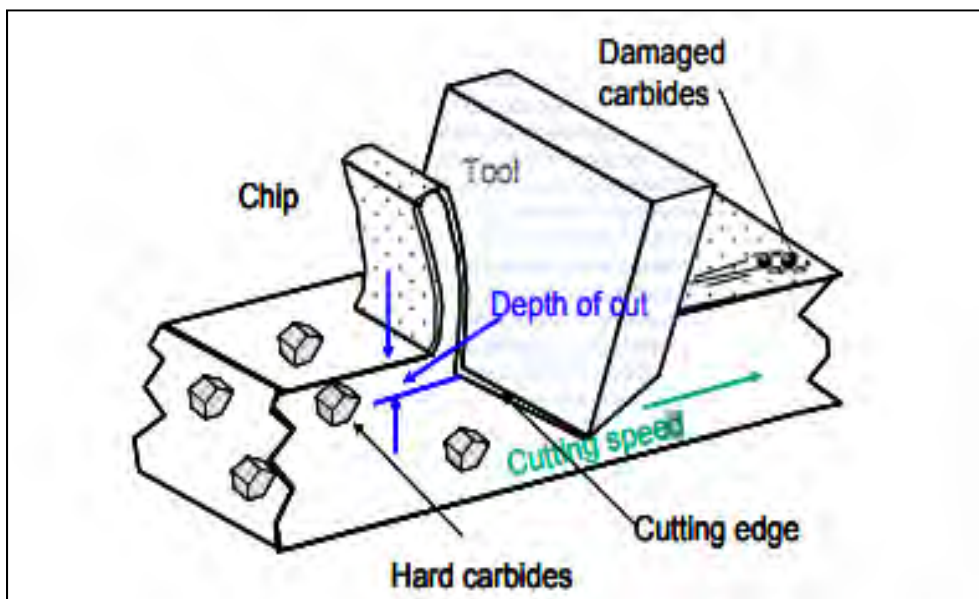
Illustration de l'effet de l'usinage sur la fissuration des carbures (Ranganath, Guo et Holt, 2009b)
